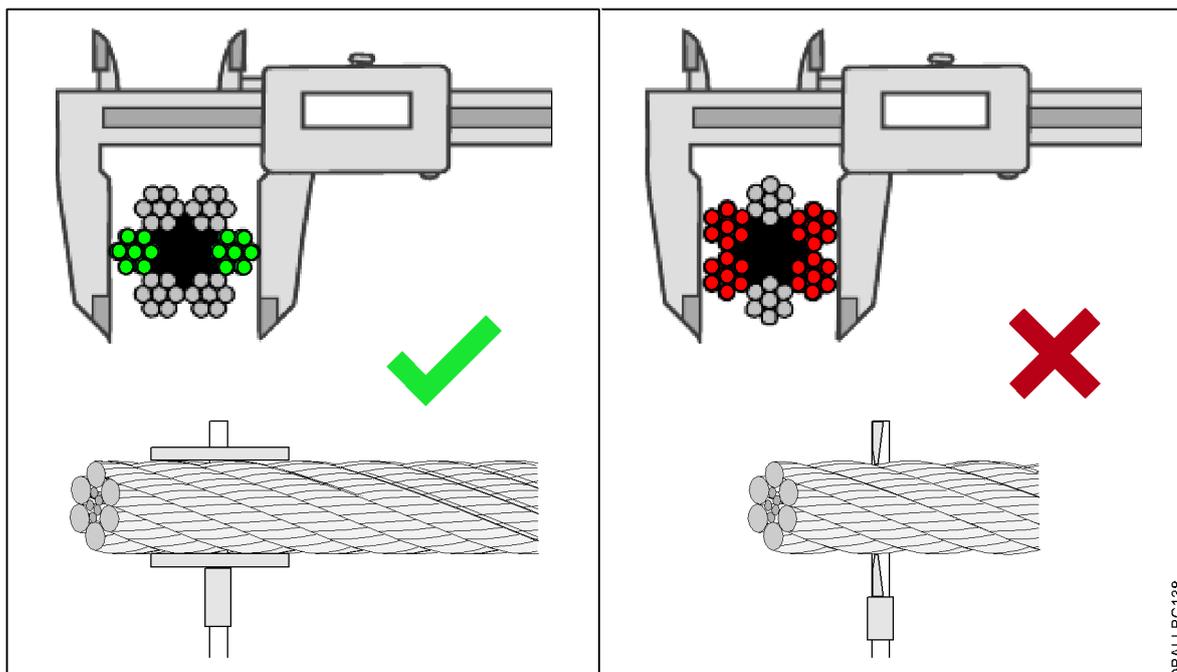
Seildurchmesser richtig gemessen (linke Seite) und falsch gemessen (rechte Seite)
